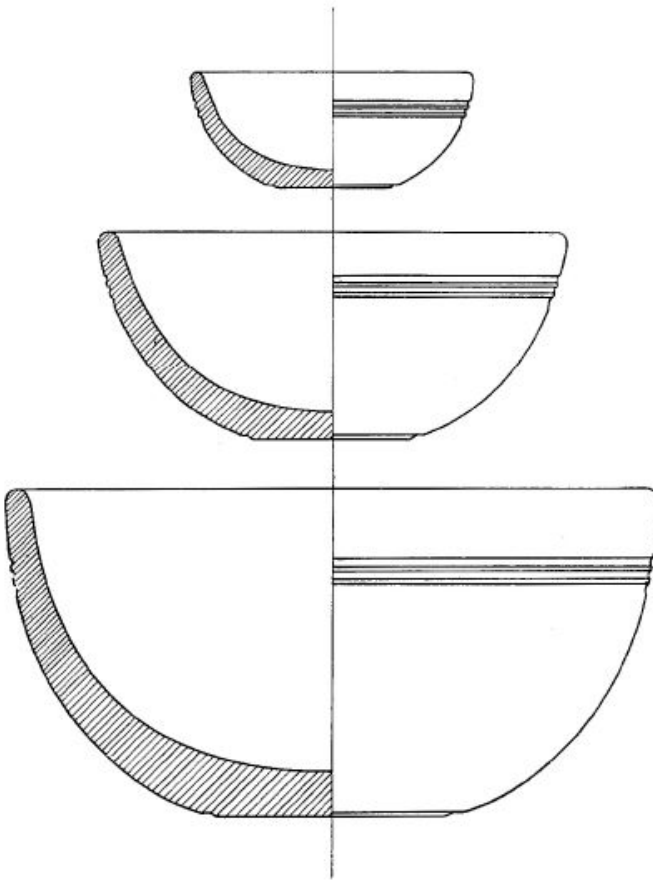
Werkzeichnung der drei einzelnen Schüsseln, wie sie sich aus dem Werkstück ergeben
